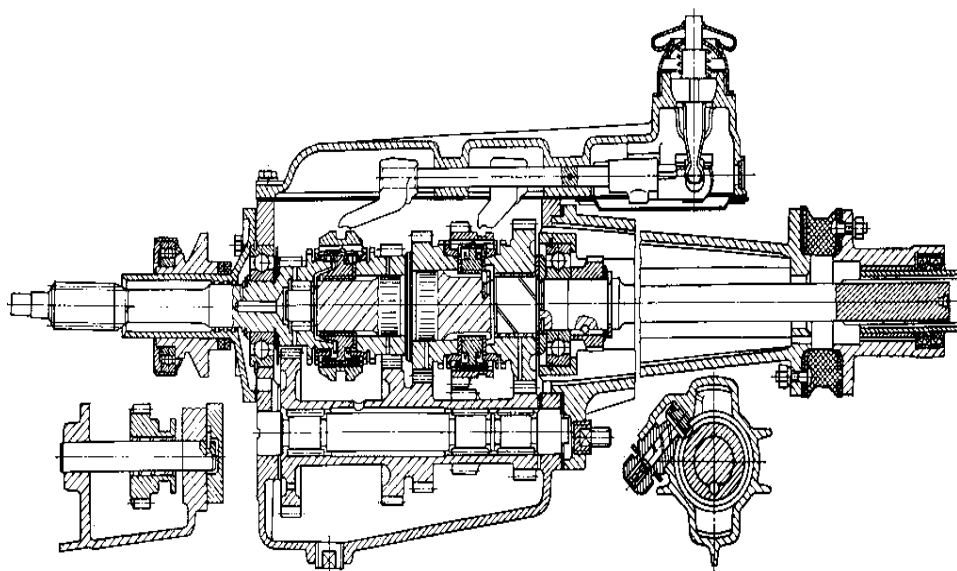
Конструкция коробки передач автомобиля ГАЗ-24
